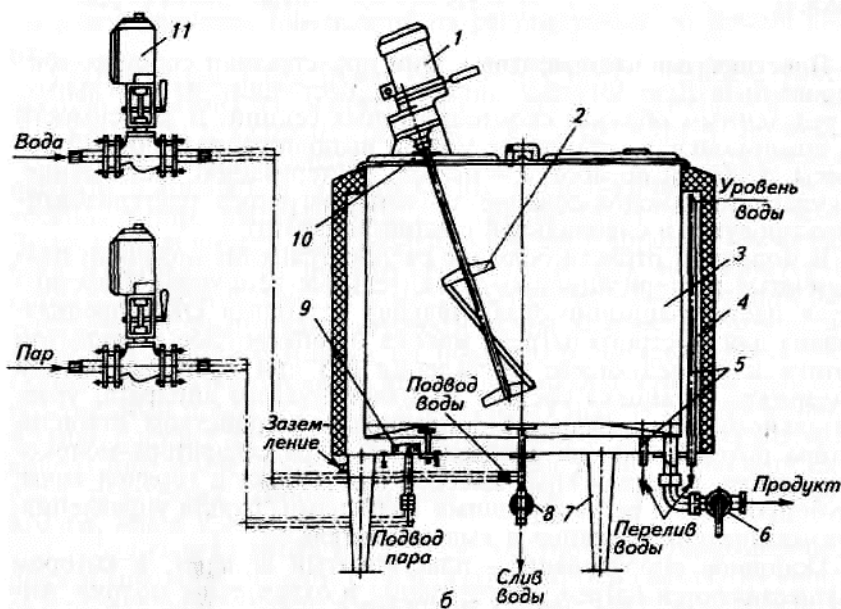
, б. Емкостное оборудование для пастеризации (ванна Г6-ОПА-600 / Г6-ОПБ-1000/): 1 – привод мешалки; 2 – мешалка; 3 – внутренняя ванна; 4 – корпус; 5 – переливные трубы; 6 – кран; 7 – опора; 8 – вентиль; 9 – распределительная головка; 10 – крышка корпуса; 11 – электромагнитный вентиль.
